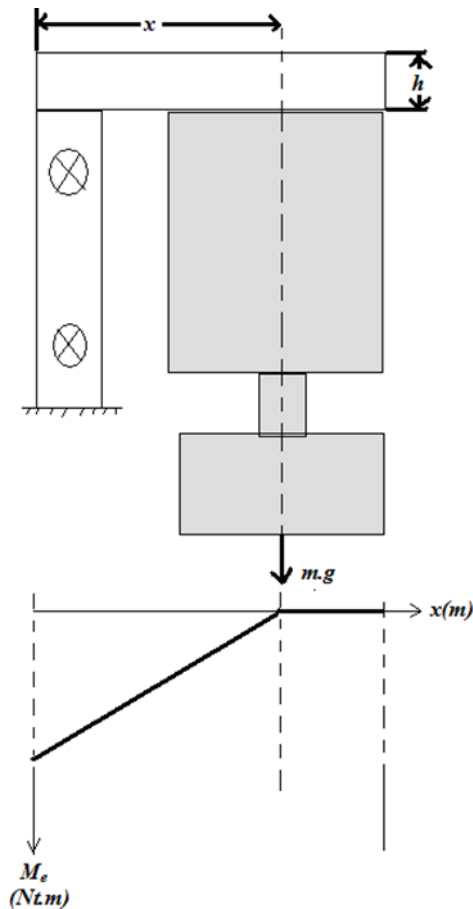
Модель згинання елементів, що тримають захват
